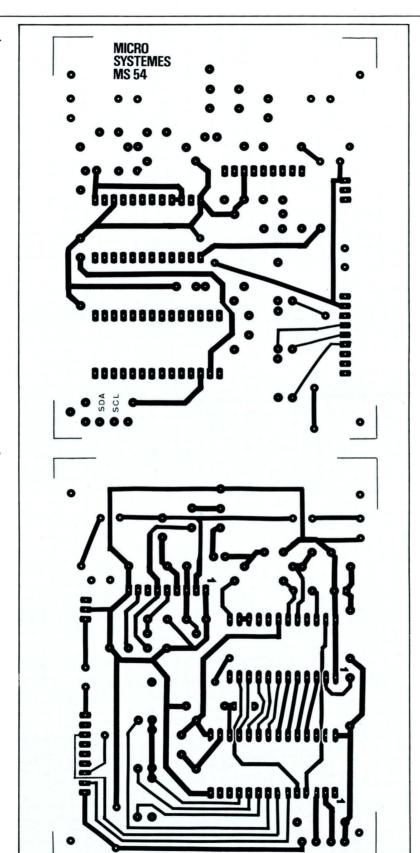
Le circuit imprimé ► (côté soudures).
